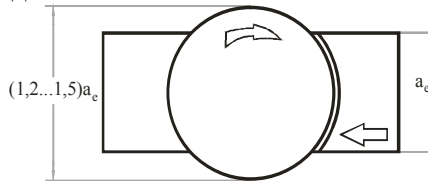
Принцип выбора диаметра торцевой фрезы
